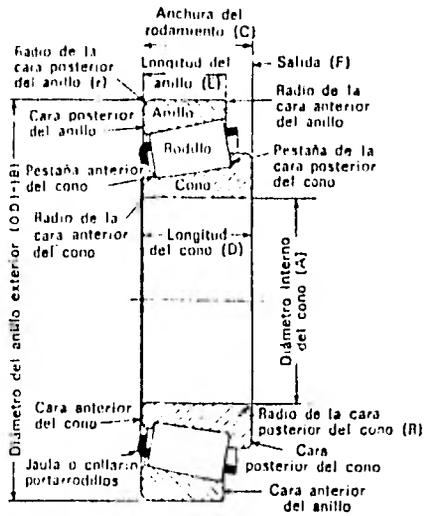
Corte de un rodamiento cónico de rodillos.
